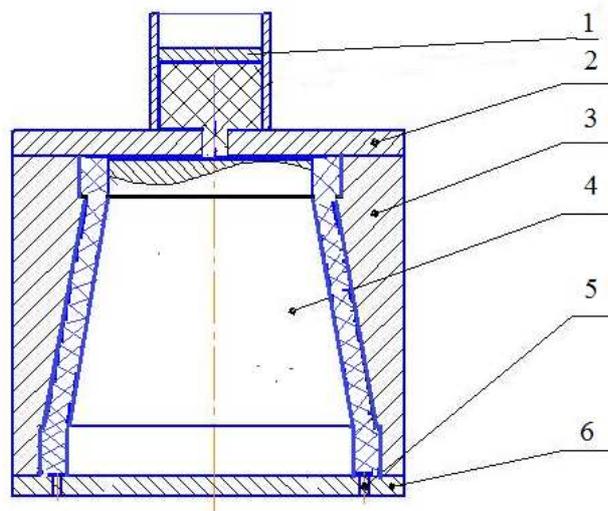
Пресс-форма для отливки стакана: 1 – поршень; 2 – крышка пресс-формы; 3 – внешняя обечайка; 4 – внутренняя вставка; 5 – воздушные каналы; 6 – основание
